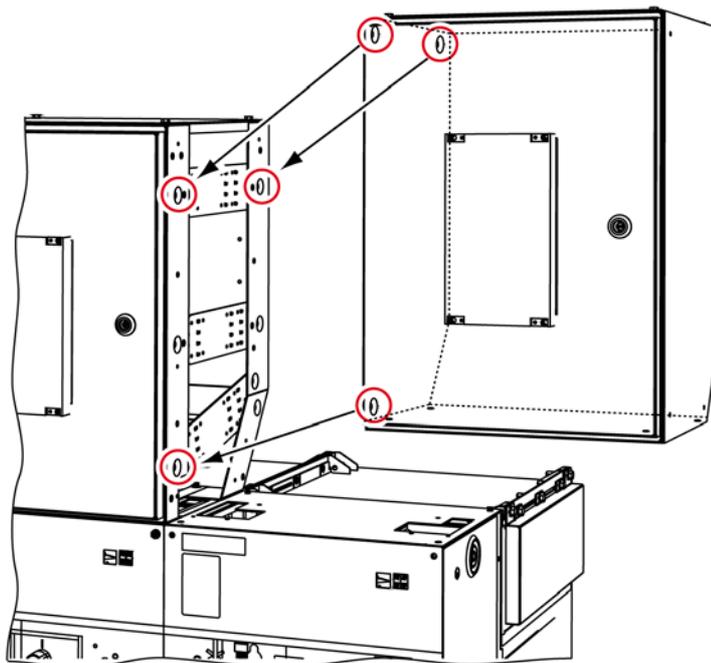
Крепление низковольтного отсека к ячейке с помощью резьбовых соединений
